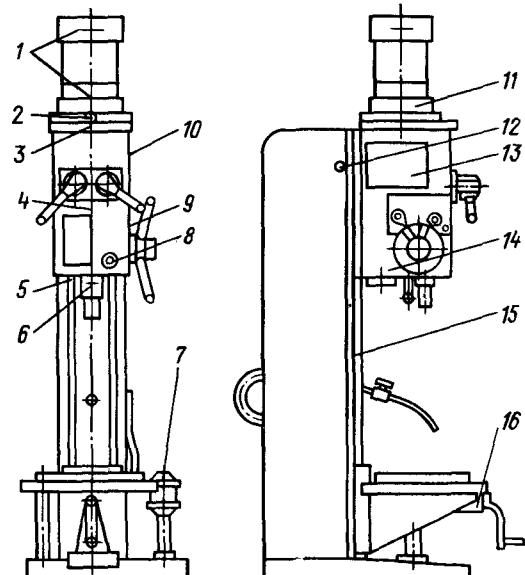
Схема смазки станков 2H125 и 2H135
